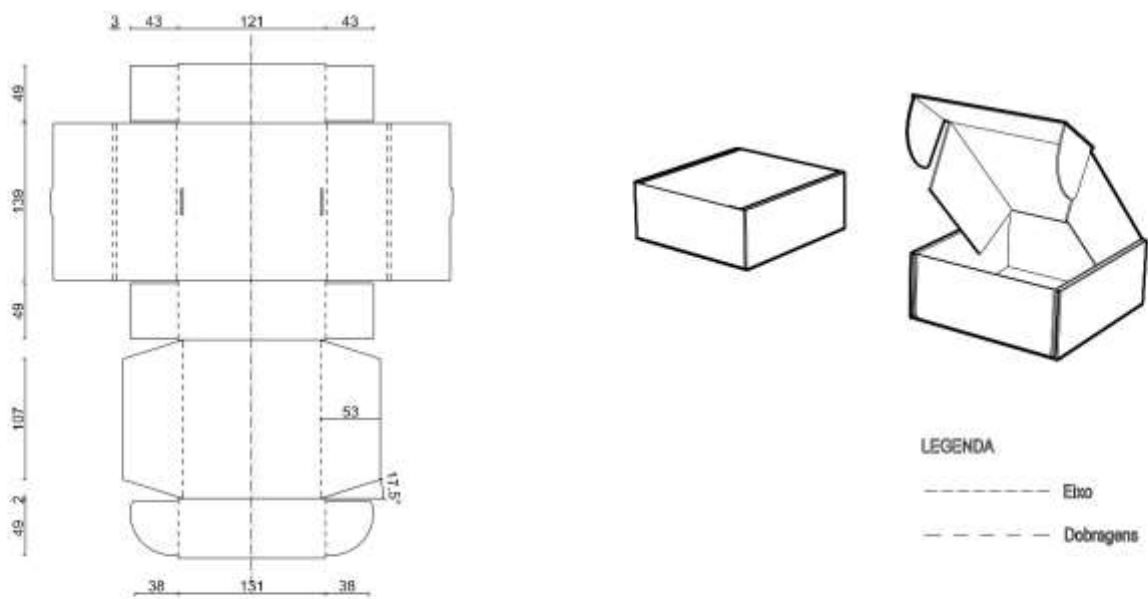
Desenho técnico embalagem exterior (Fonte: o autor)
